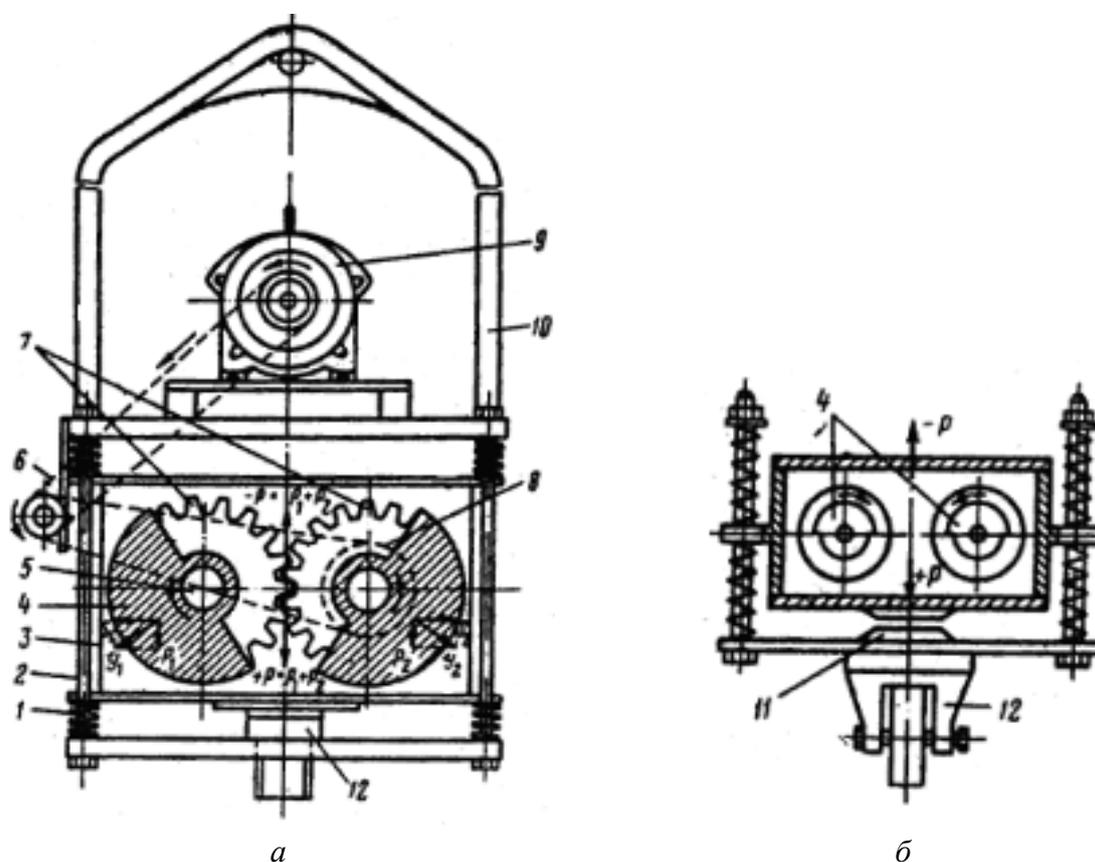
Вибрационные машины: *а* – двухблочный вибратор; *б* – вибромолот; 1 – пружина; 2 – болт; 3 – корпус вибратора; 4 – эксцентрики; 5 – валики; 6 – клиноременная передача; 7 – шестерни; 8 – шкив; 9 – электродвигатель; 10 – серьга; 11 – наковальня; 12 – переходник
